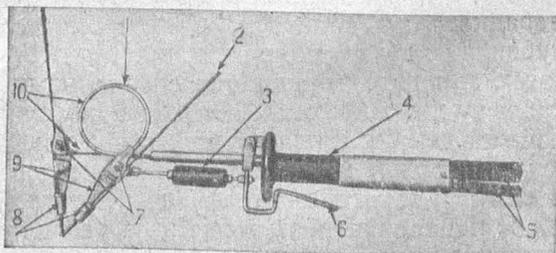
Держатель для атомно-водородной сварки. 7 — вольфрамовый электрод.
